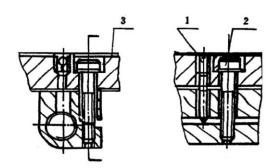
Схема регулировки винтовой гайки вертикального суппорта
